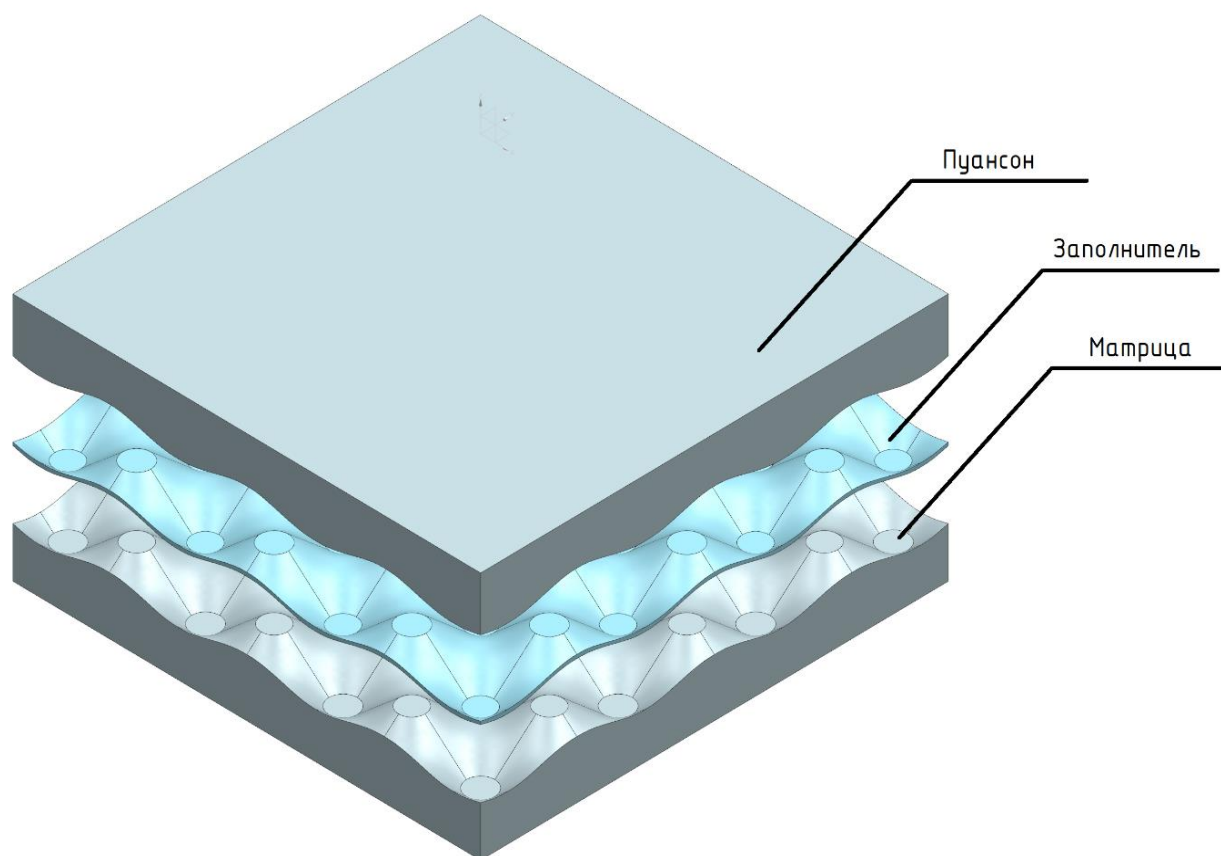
Схема процесса холодной штамповки заполнителя
